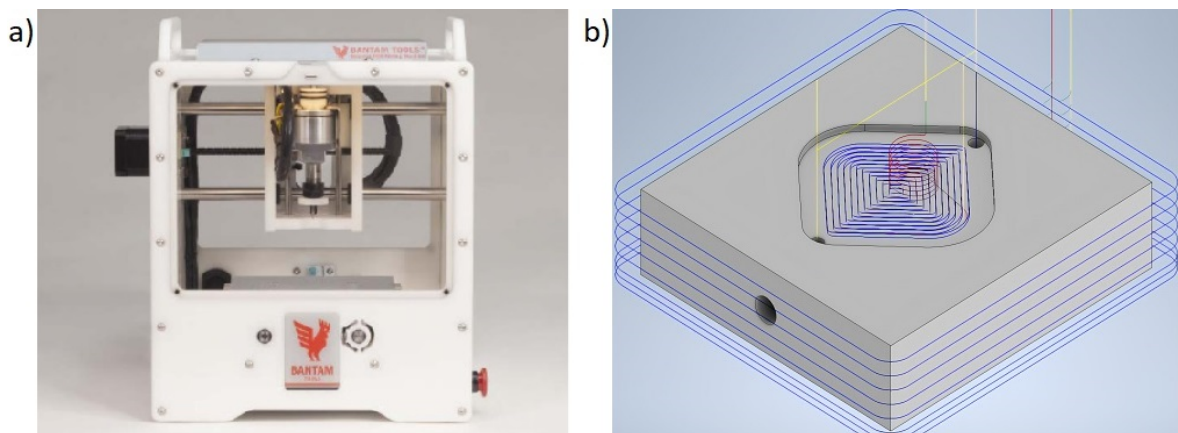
a) Bantam Tools PCB Milling Machine; b) Modelo 3D do canal microfluídico e os caminhos percorridos pela fresa no primeiro processo de usinagem.
